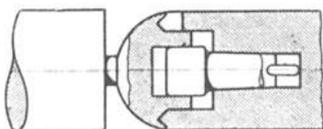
Schlichten der Ringnut mit Bohrstange.
